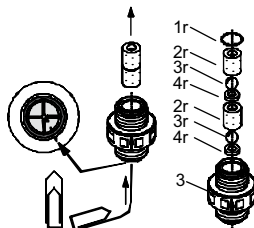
Конструкция. Стандартный клапан DN 4/DN 8
